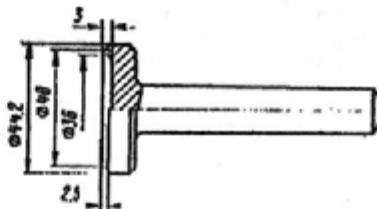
Оправка для установки стопорной шайбы манжеты усилителя
